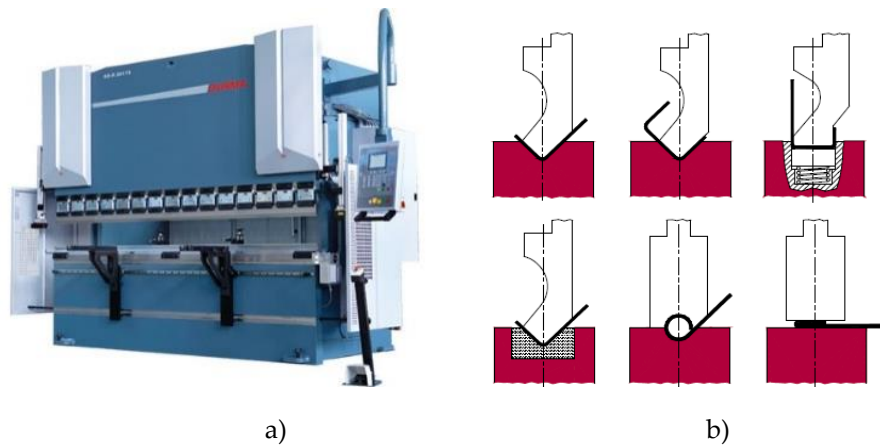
Quinadora (a) e ferramentas de quinagem (matriz e punção)(b) [10]
